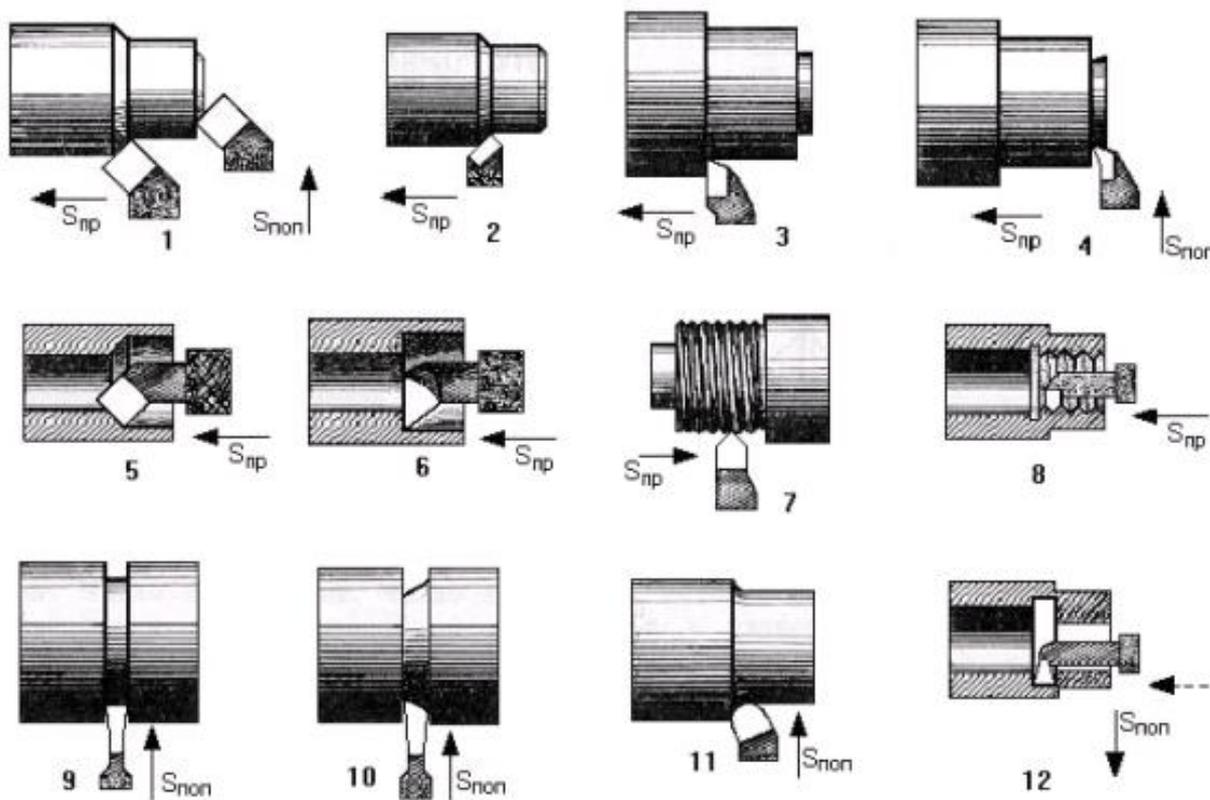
Типы токарных резцов: 1 – проходной отогнутый; 2 – проходной прямой; 3 – проходной упорный; 4 – подрезной; 5 – расточной отогнутый; 6 – расточной подрезной; 7, 8 – резьбовые; 9 – прорезной (канавочный); 10 – отрезной; 11 – галтельный; 12 – расточной упорный.
